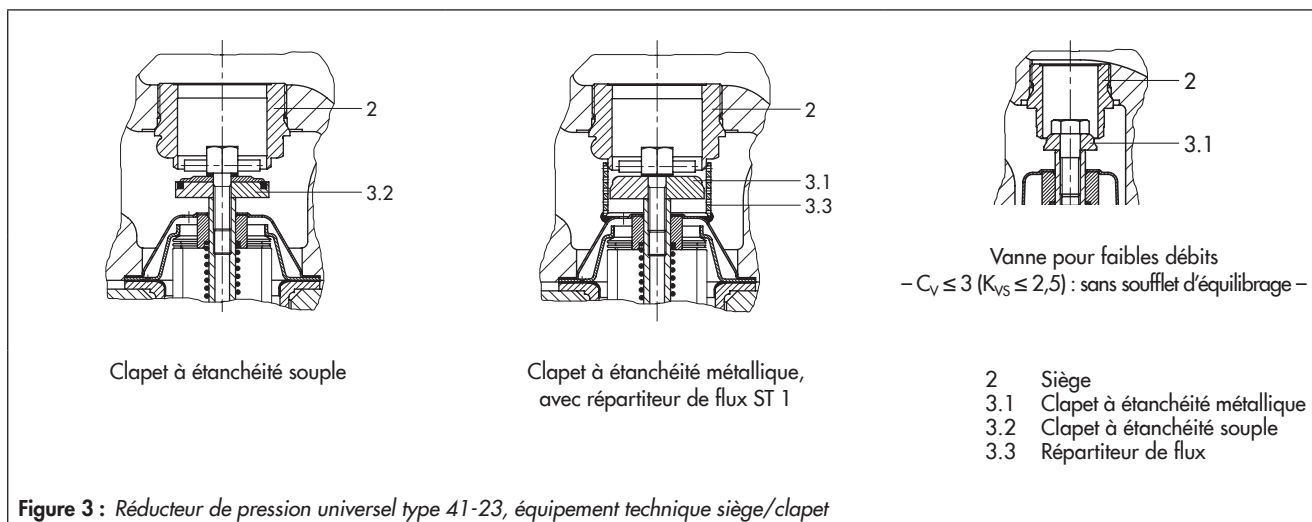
Réducteur de pression universel type 41-23, équipement technique siège/clapet
